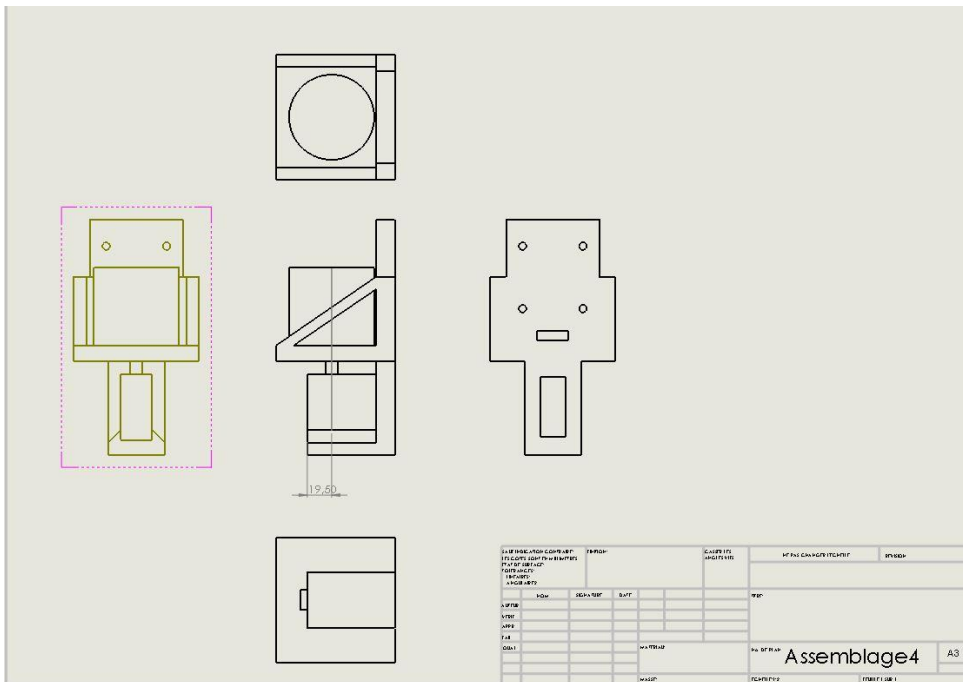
Dessin d'assemblage cible, moteur et cuve.
